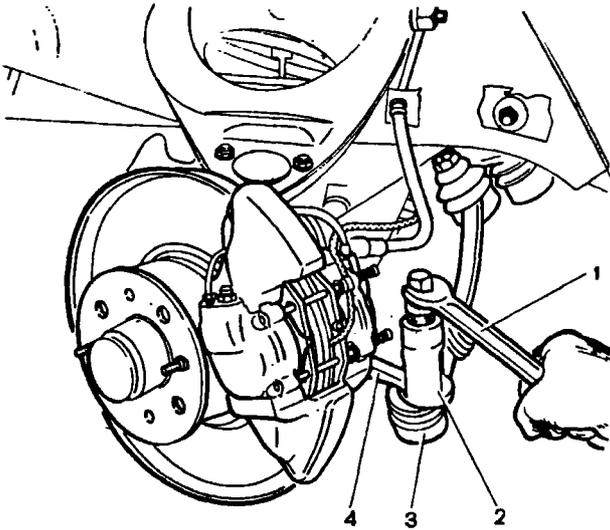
Снятие шаровых пальцев тяг рулевой трапеции: 1 - ключ гаечный; 2 - съемник А.47052; 3 - шаровой шарнир; 4 - рычаг поворотного кулака
